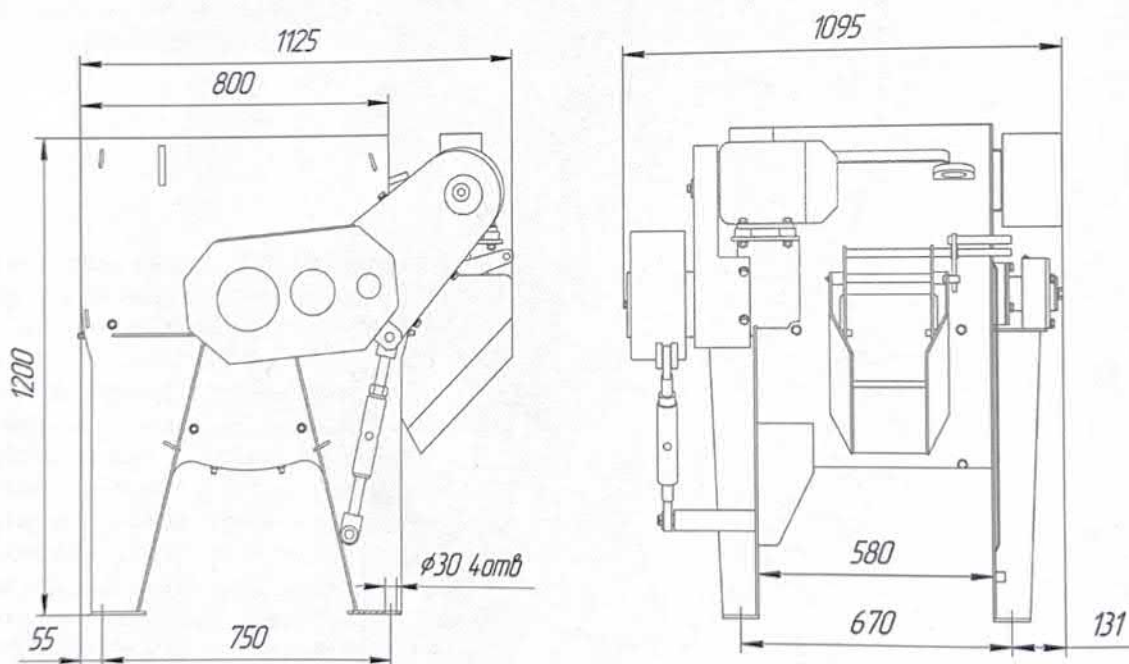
Габаритно-присоединительные размеры СГ-150.
